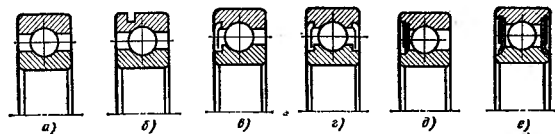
Шарикоподшипники радиальные однорядные типов: а — 00000; б — 50000; в — 60000; г — 80000; д — 160000; е — 180000
